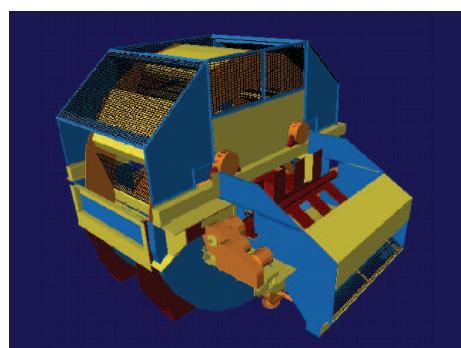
Колесный сепаратор с вертикальным элеваторным кольцом
